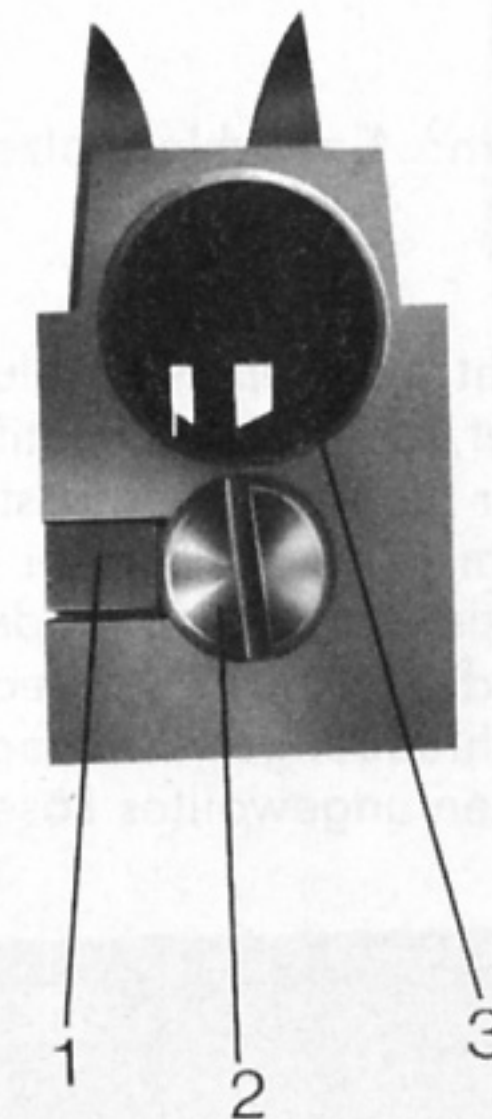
Verschußzylinder von hinten: 1 = Schlagbolzen, 2 = Gewindestift für Schlagbolzenfeder, 3 = Lager für Vorholfeder.
